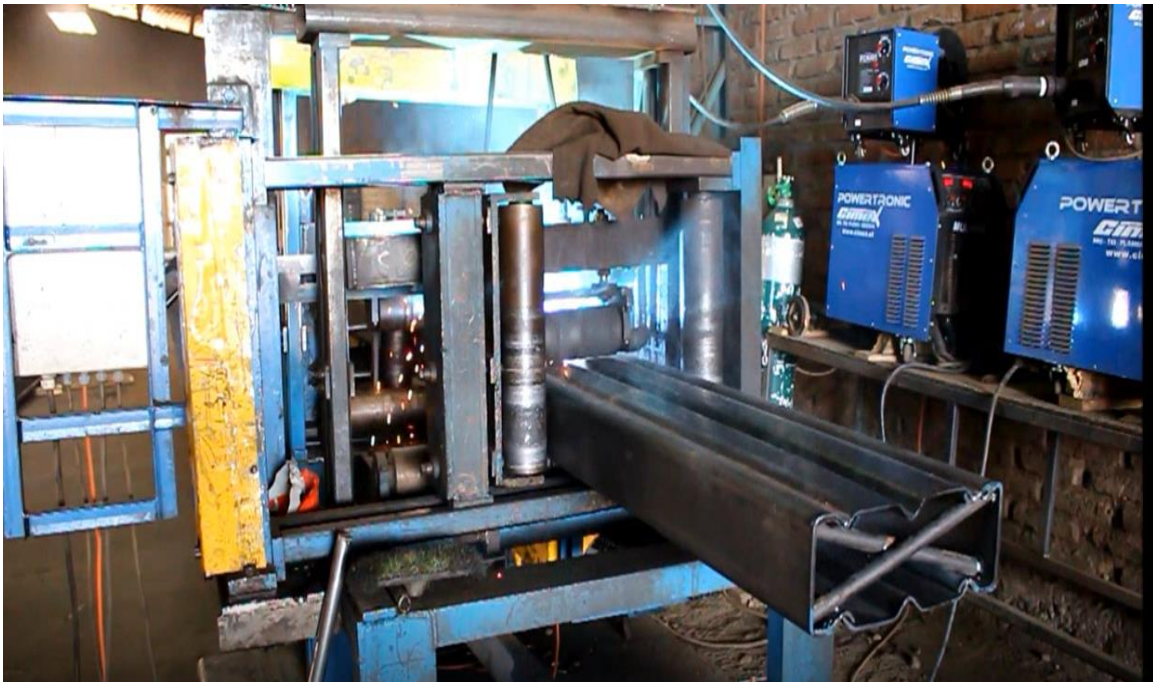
Soldadura MIG en taller de Tupemesa
